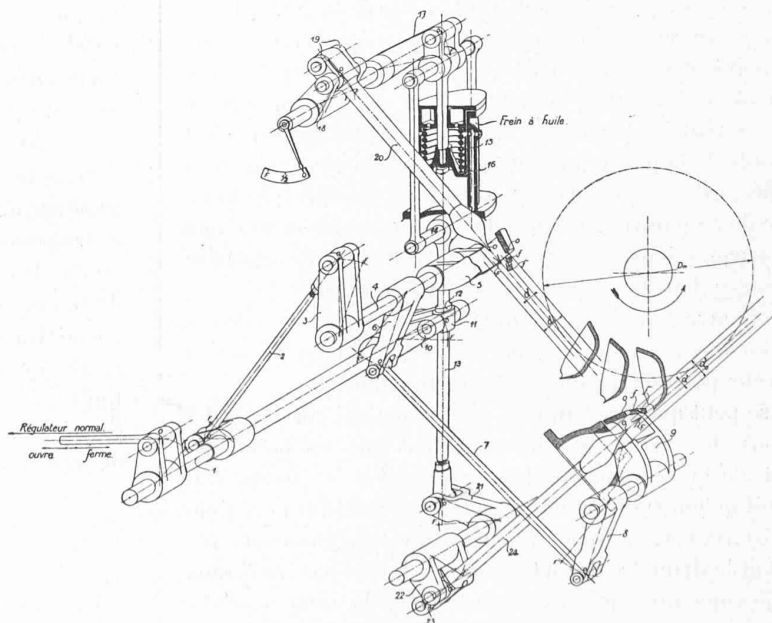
Schéma perspectif du régulateur à double action de la turbine Pelton de 2000 HP.
